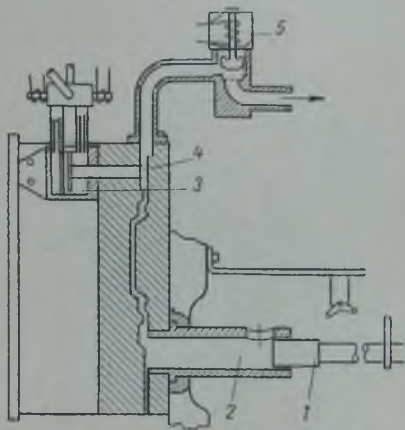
Схема вакуумного приспособления для машин литья под давлением
